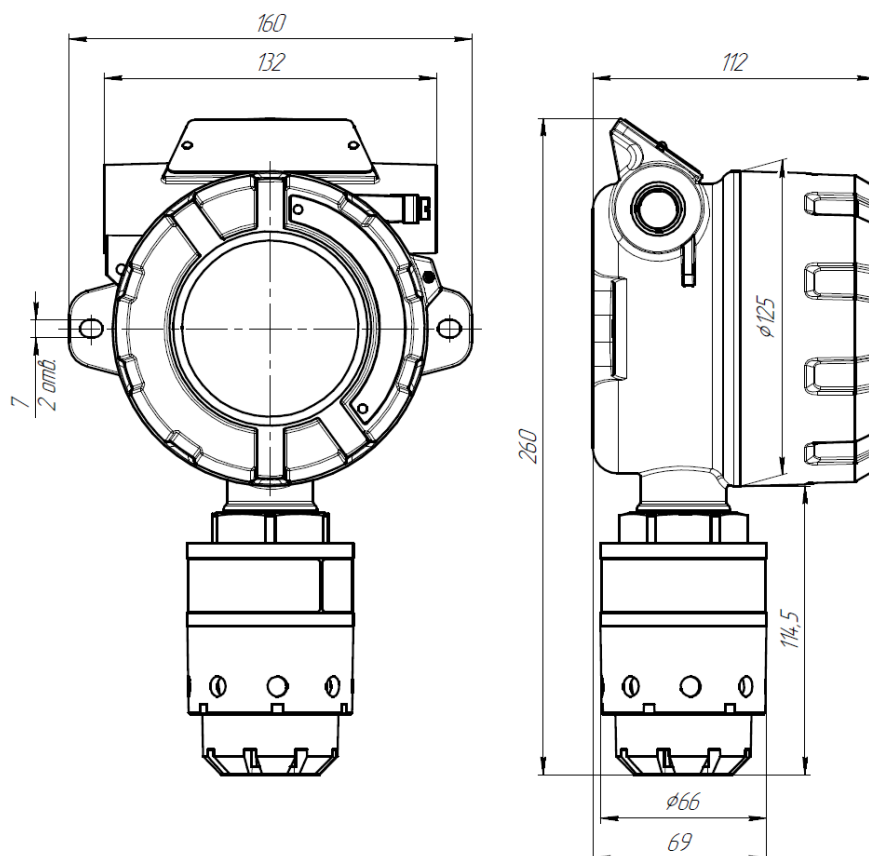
Габаритные размеры газоанализатора в корпусе типа Б
